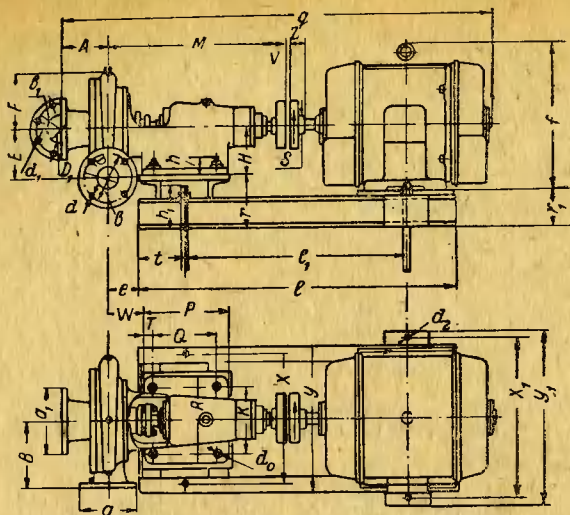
Центробежный насос „НК“ (габаритный чертеж)
